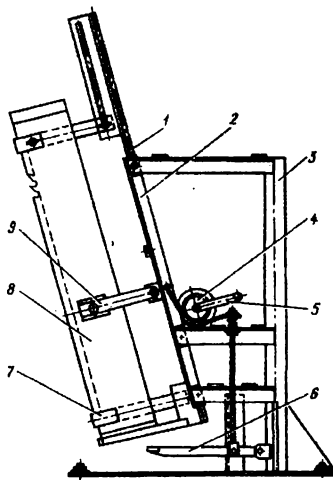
Приспособление для установки рамной пилы при наплавке зубьев стеллитом
